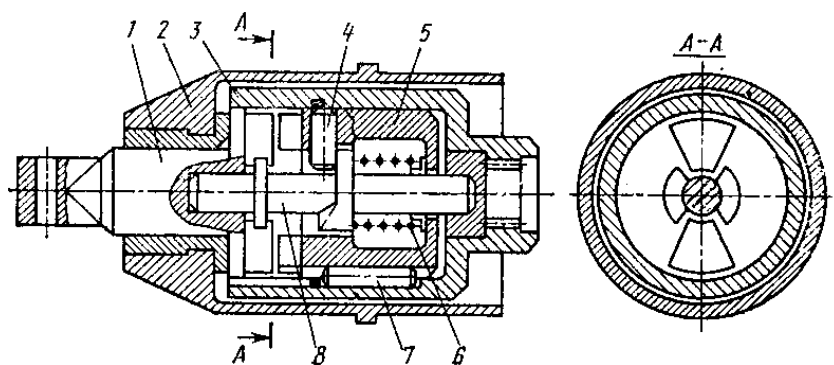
Ударный механизм с кинематическим зацеплением бойка и наковальни:
